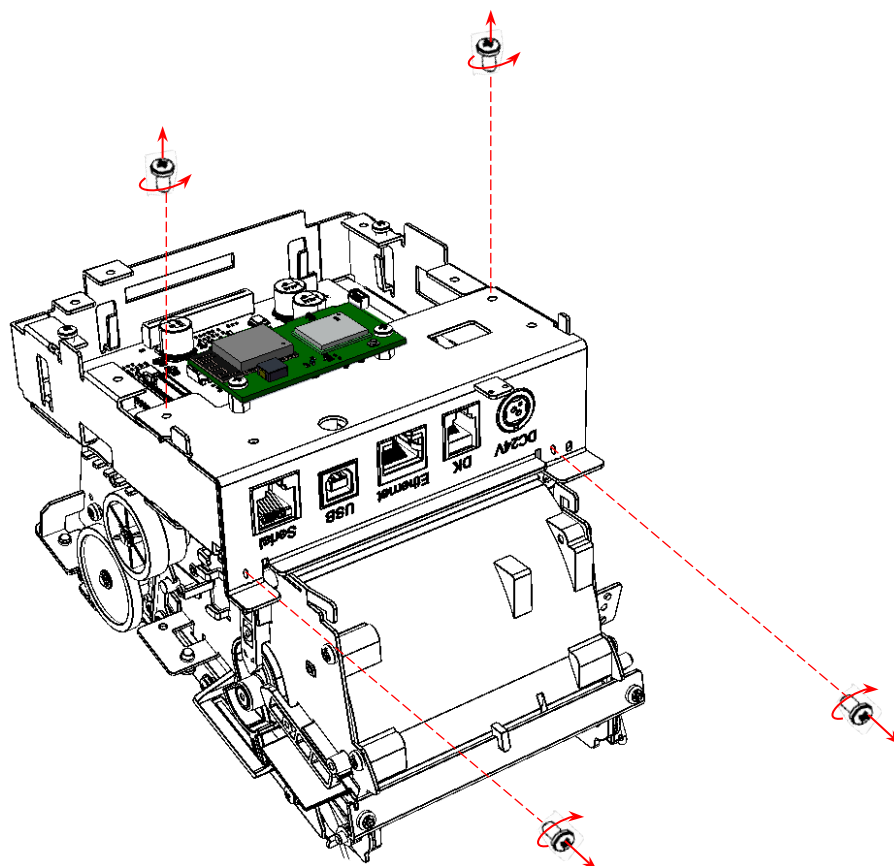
Винты крепления металлической панели к корпусу печатающего устройства
